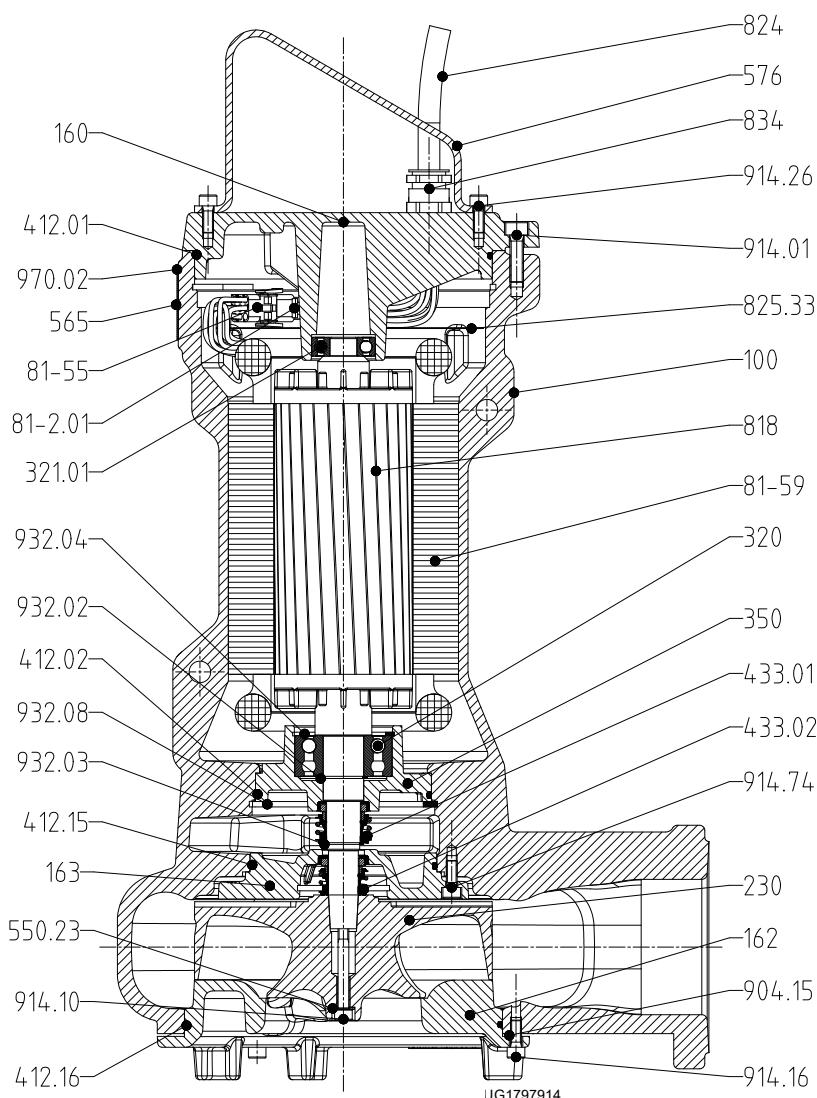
Сборочный чертеж для исполнения US, с рабочим колесом D-max
